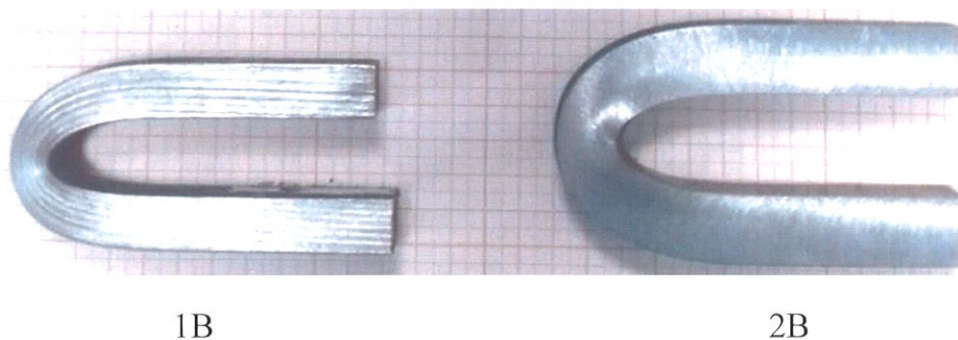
Внешний вид образцов после испытаний на изгиб
